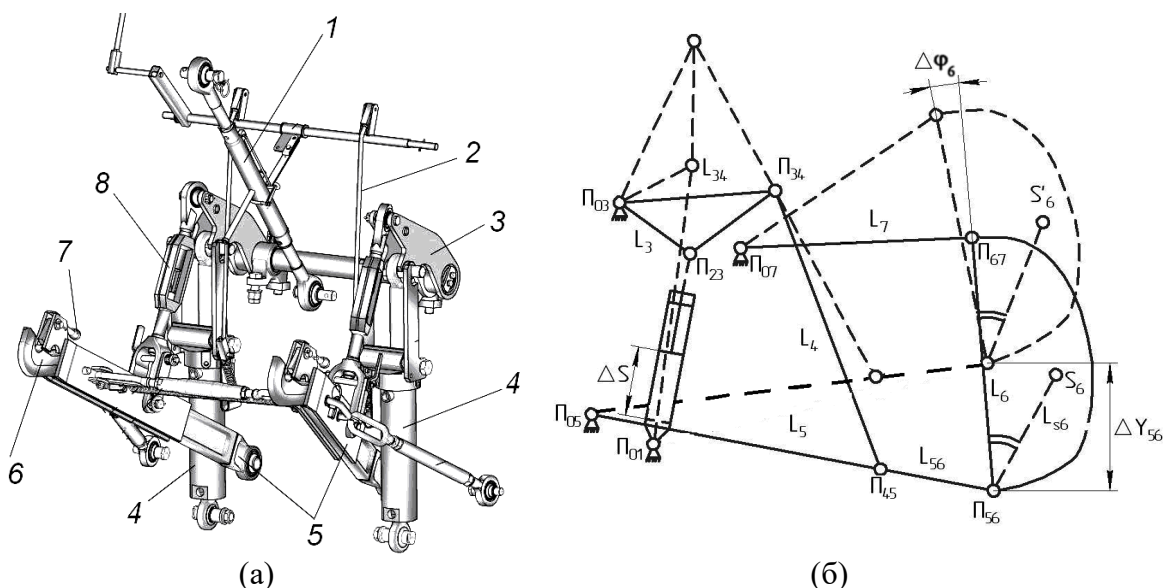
Подъемно-навесное устройство (а) и схема плоского аналога механизма навески в рабочем и транспортном положениях (б) 1 – тяга верхняя; 2 - тяга механизма фиксации; 3 – рычаг поворотный; 4 - гидроцилиндры; 5 – тяги нижние; 6 – захват; 7 – ручка фиксатора; 8 – раскос.
